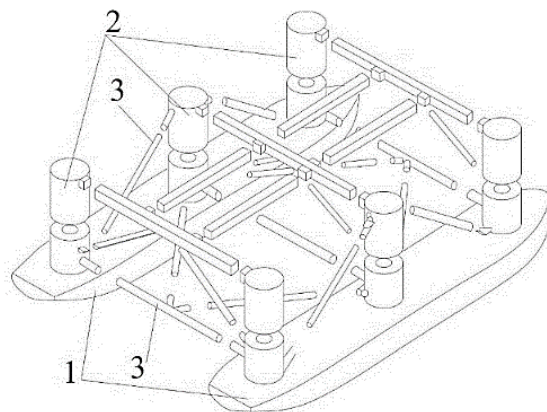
Разбивка конструкций ППБУ на сборочно-монтажные единицы (нижняя часть):
